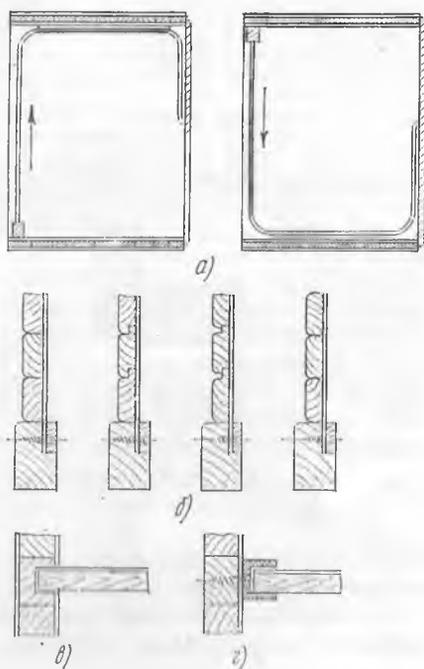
Установка шторных дверей: а — схемы установки, б — профили шторных дверей, в — установка шторных дверей в пазу, выбранном в щите, г — то же, в направляющих планках
